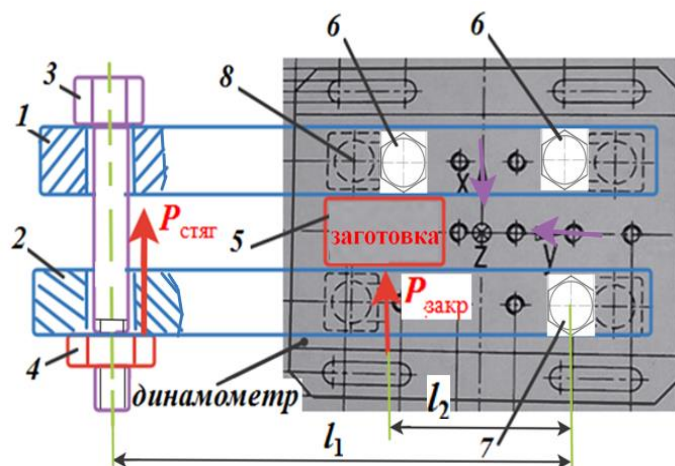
Схема закрепления небольшого образца на динамометре Kistler для фрезерования концевой фрезой
